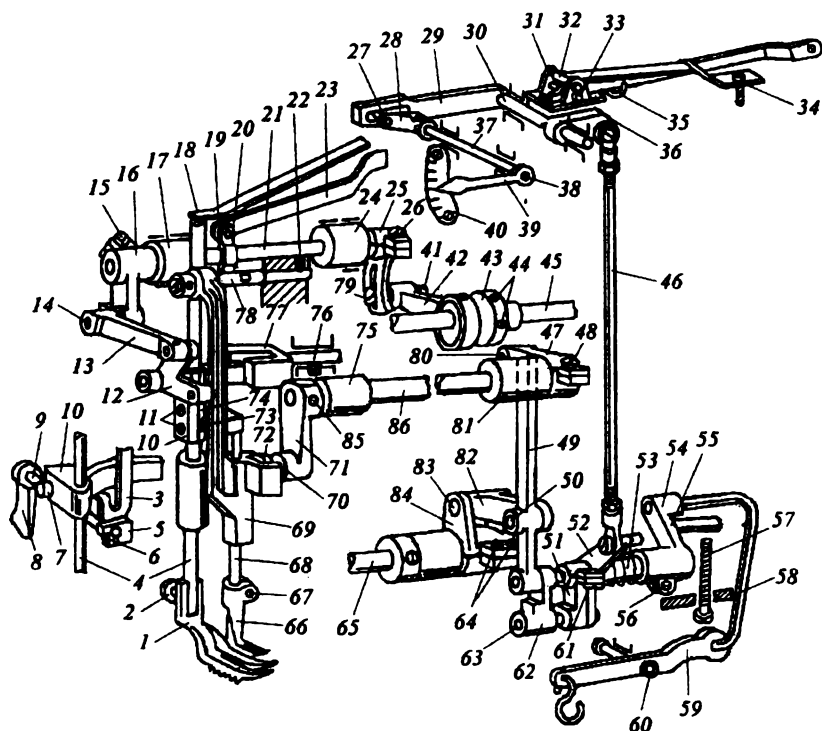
Механизм движения верхней рейки и лапки машины 302-2 кл. ПМЗ
